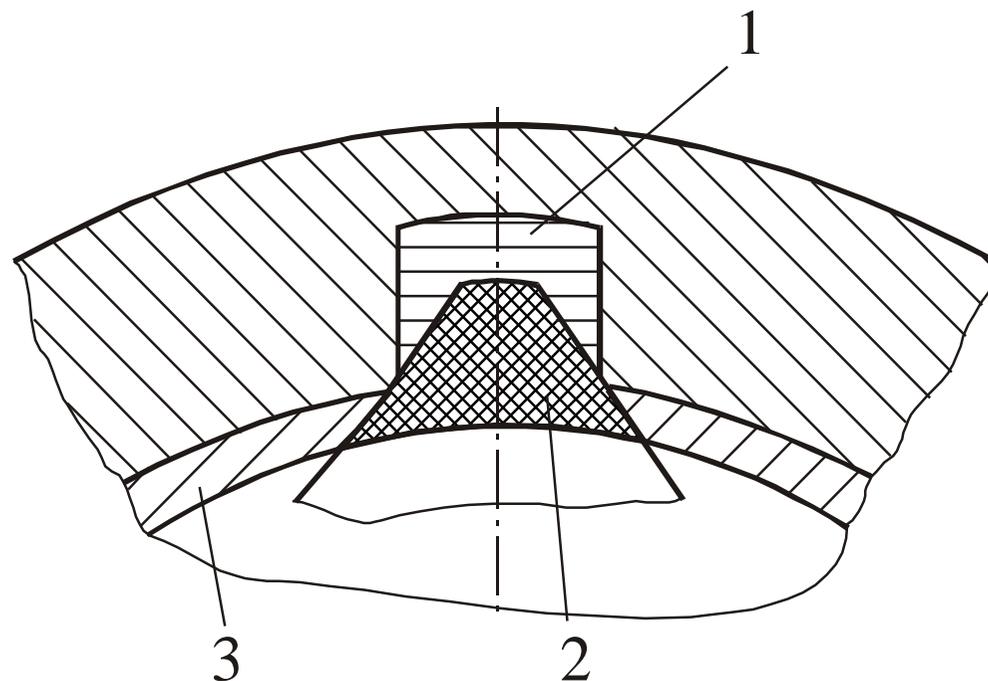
Припуск, снимаемый зубьями комбинированной шлицевой протяжки: 1 – шлицевыми; 2 – фасочными; 3 – круглыми
